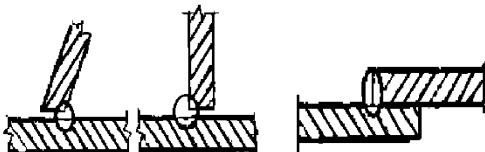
Виды сварных соединений, выполненных подводной сваркой
